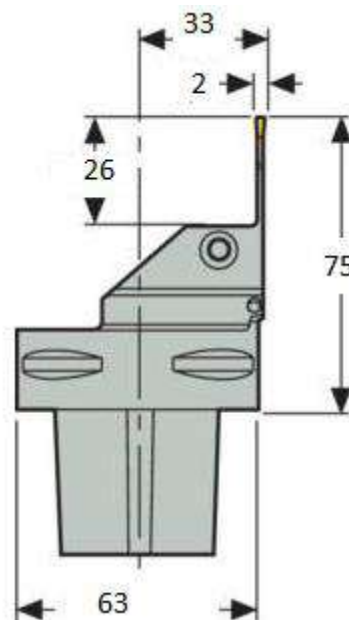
Резец С6-CFZL-33075-2802JET
